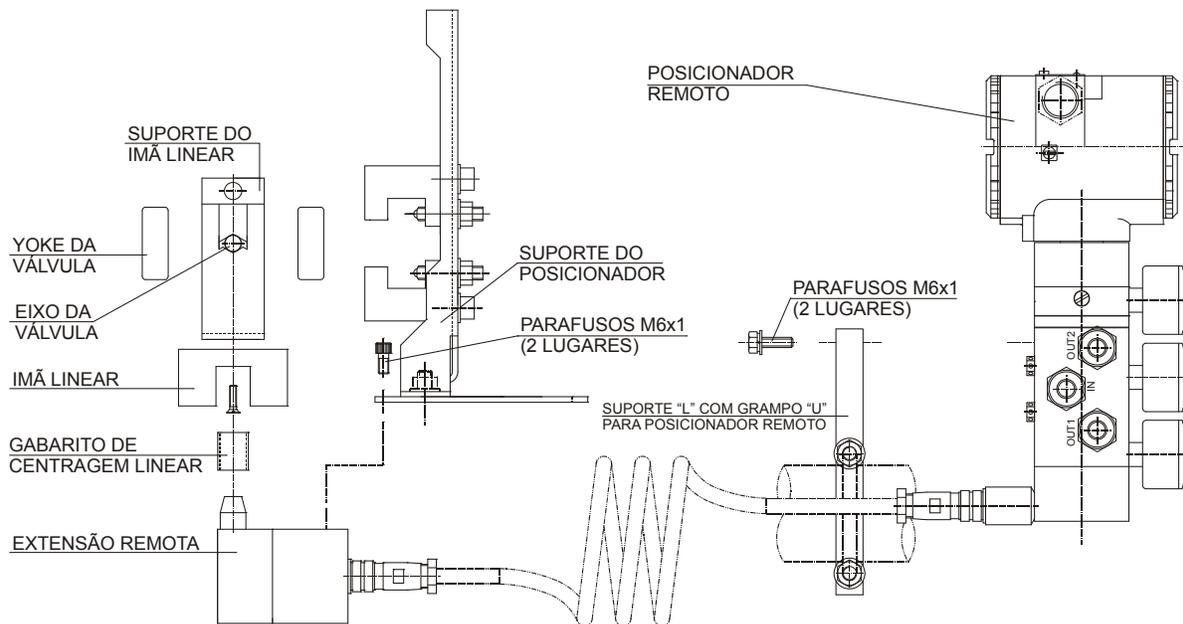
Posicionador em Atuador Linear com Sensor de Posição Remoto
